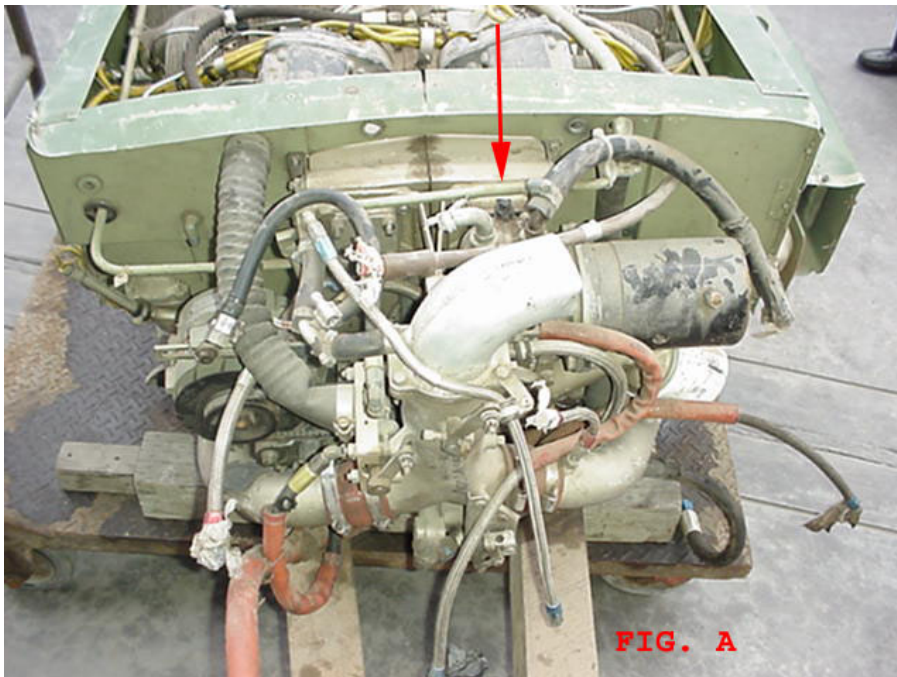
FIG A. detalle de la posición de la bomba de combustible, en la parte posterior del motor.
